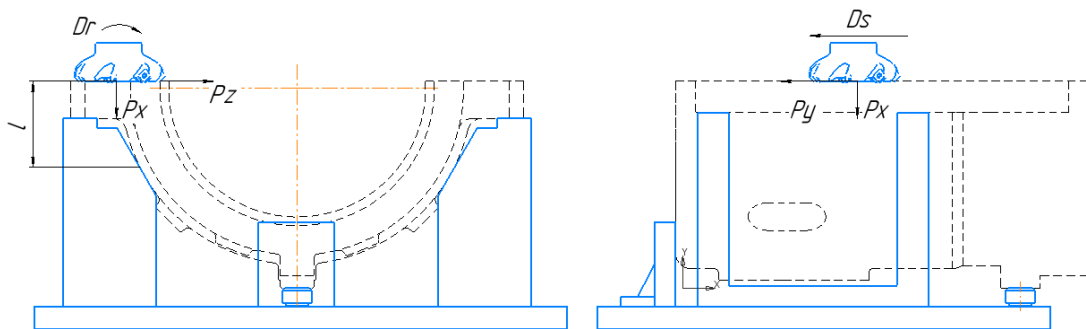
Эскиз заготовки и действующая на неё сила резания
